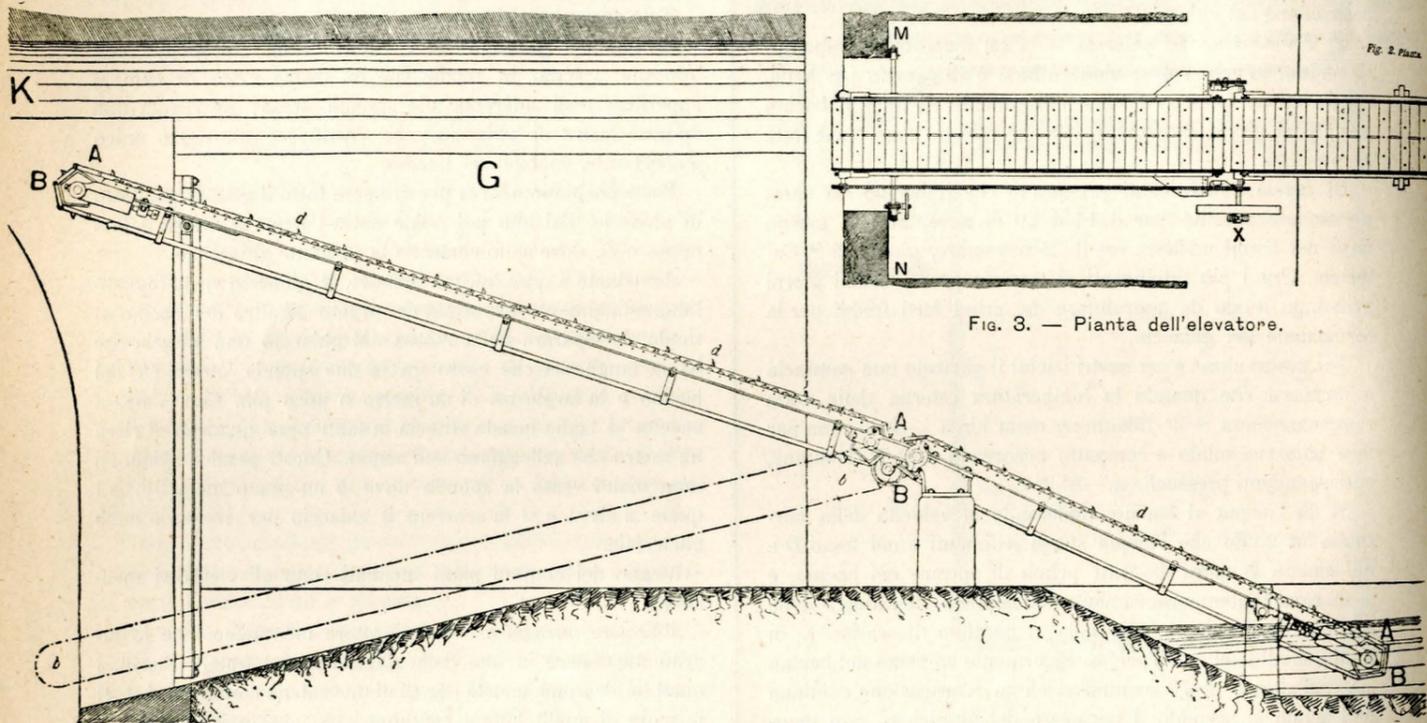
Elevatore del ghiaccio (Sezione verticale).
